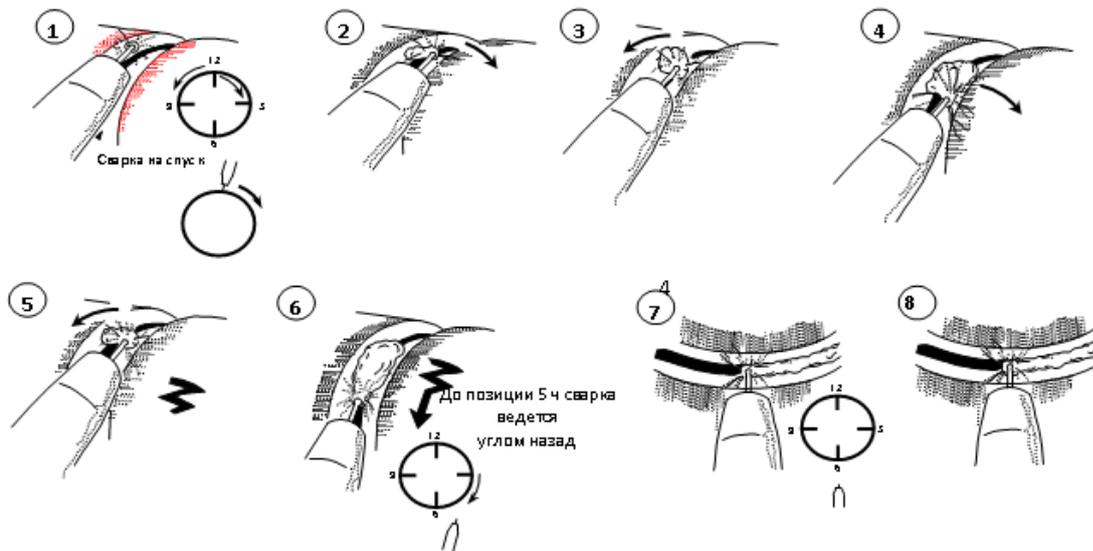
Техника механизированной сварки корневого слоя шва
